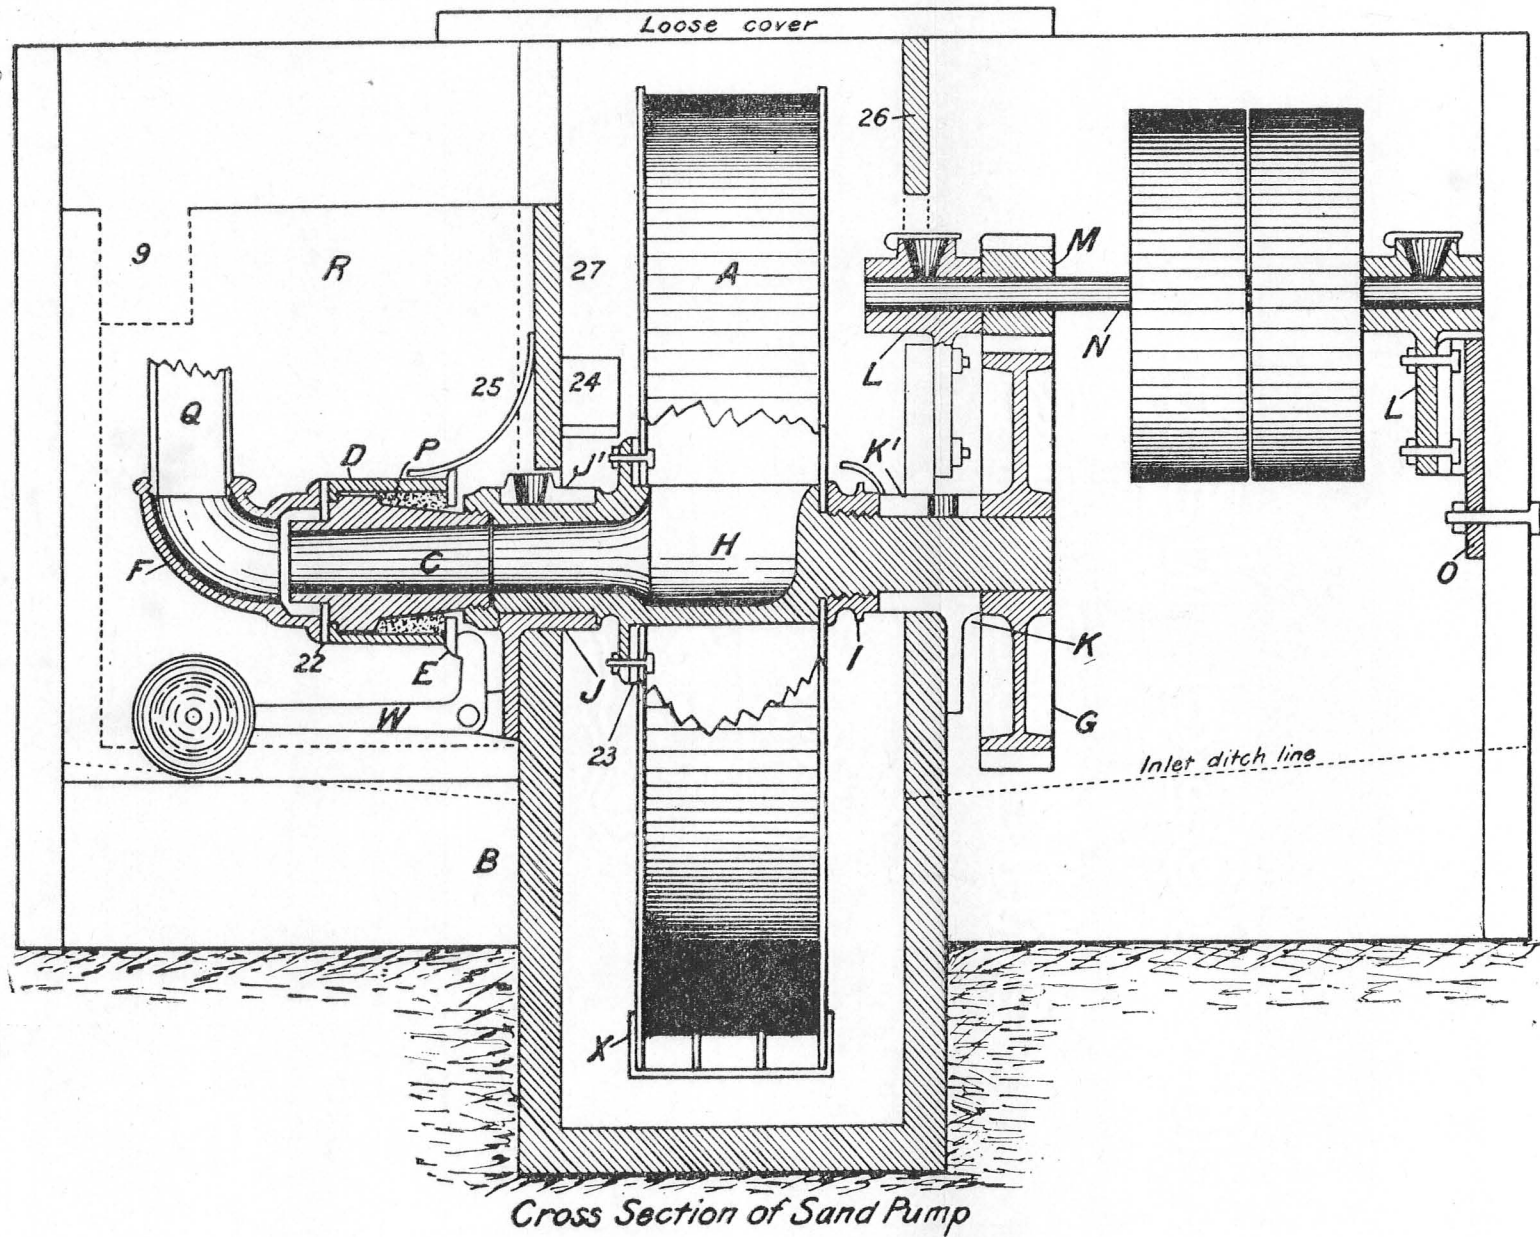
Détails de la pompe spirale Frenier, pour enlever le sable.
